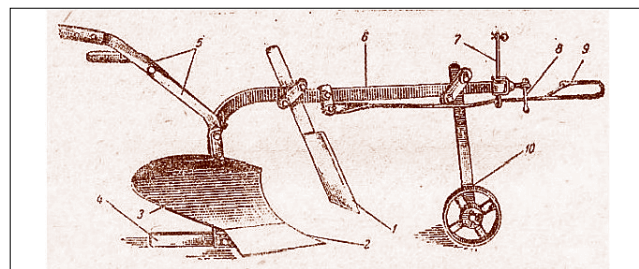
Висячий плуг ПВ-23: 1 – черенковый нож; 2 – лемех; 3 – отвал; 4 – полевая доска; 5 – ручка; 6 – грядиль; 7 – регулятор глубины вспашки; 8 – регулятор ширины захвата; 9 – упряжной крюк; 10 – колесо с поддерживающей стойкой
